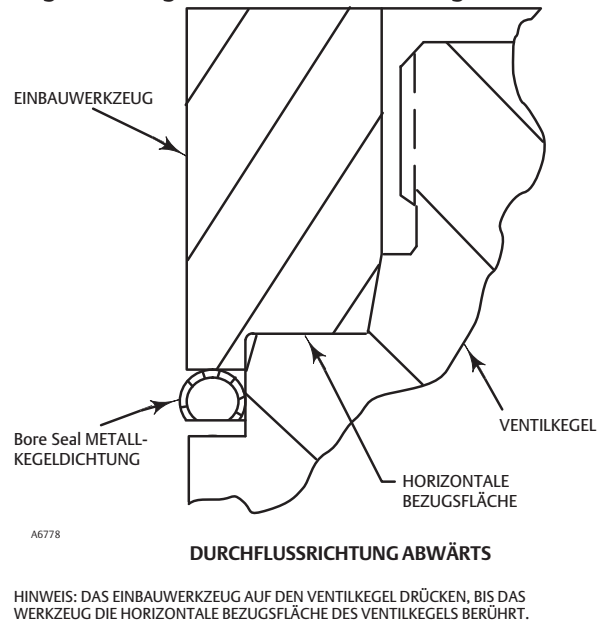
Installieren der Bore Seal Kegeldichtung mit dem Einbauwerkzeug
